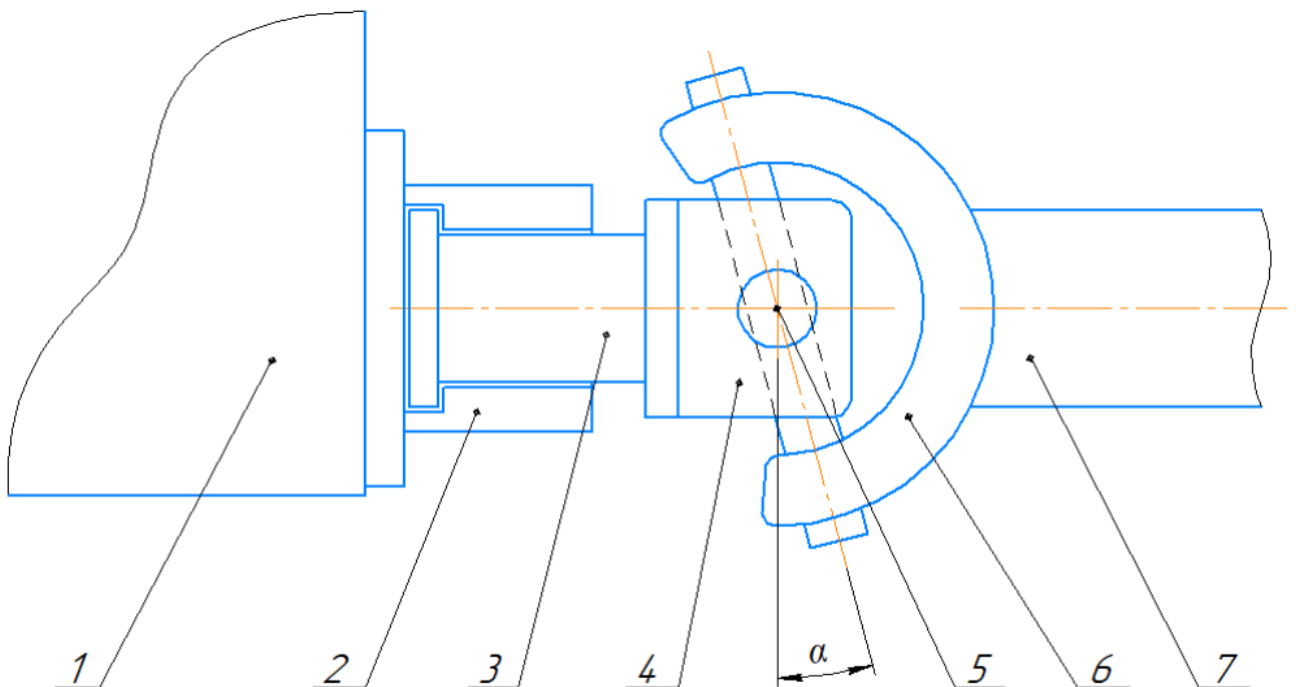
Схема стабілізуючого тягово-зчіпного пристрою (вигляд зліва)
